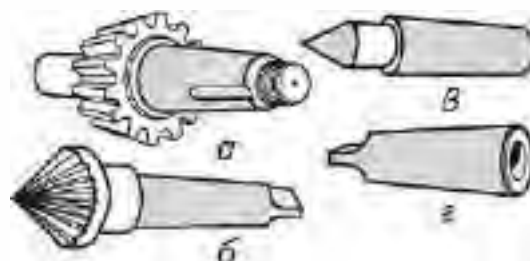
ТИПОВІ ДЕТАЛІ З КОНІЧНИМИ ПОВЕРХНЯМИ
